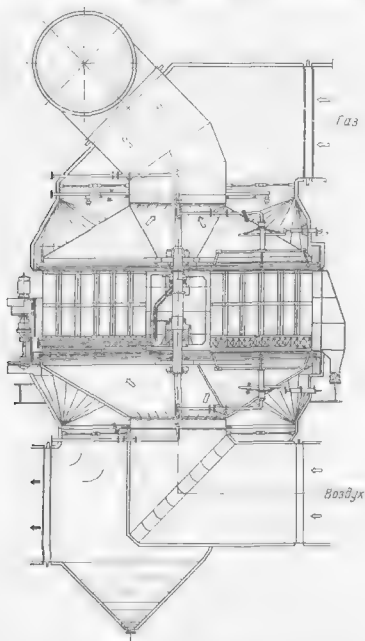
Общий вид воздухоподогревателя «Ротемюле»
